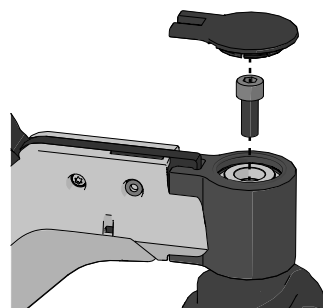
Entfernen Sie die Abdeckung und lösen Sie die Schraube.
